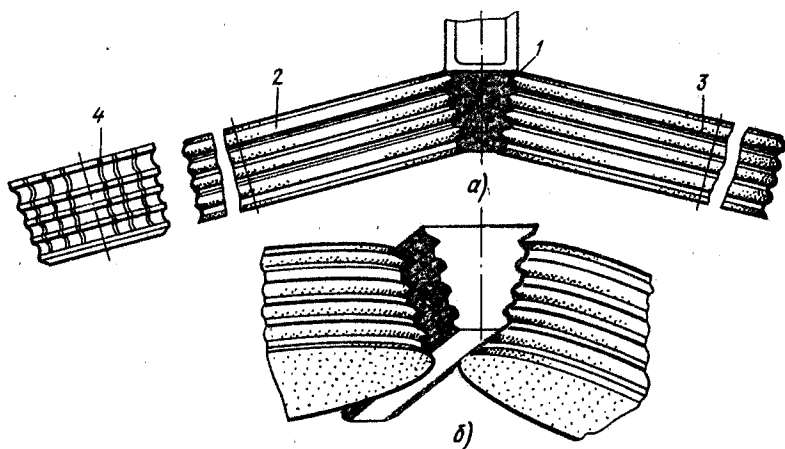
Рабочая зона станка для шлифования елочного профиля замка турбинной лопатки:
